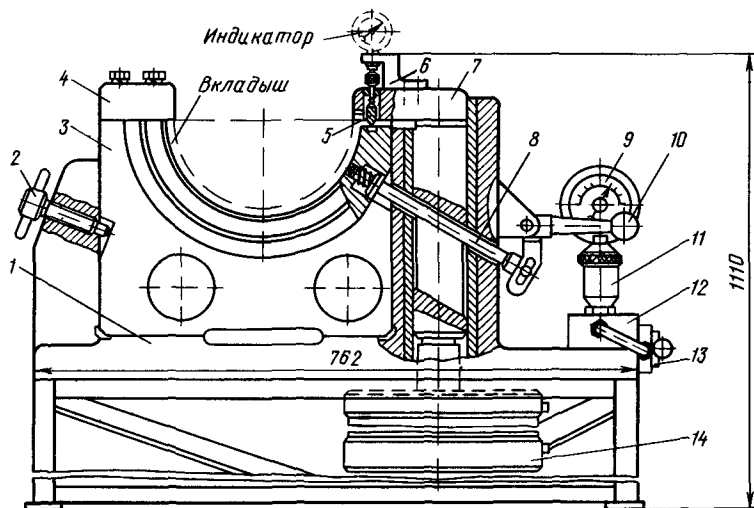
Приспособление для проверки натяга вкладыша дизеля под нагрузкой:
